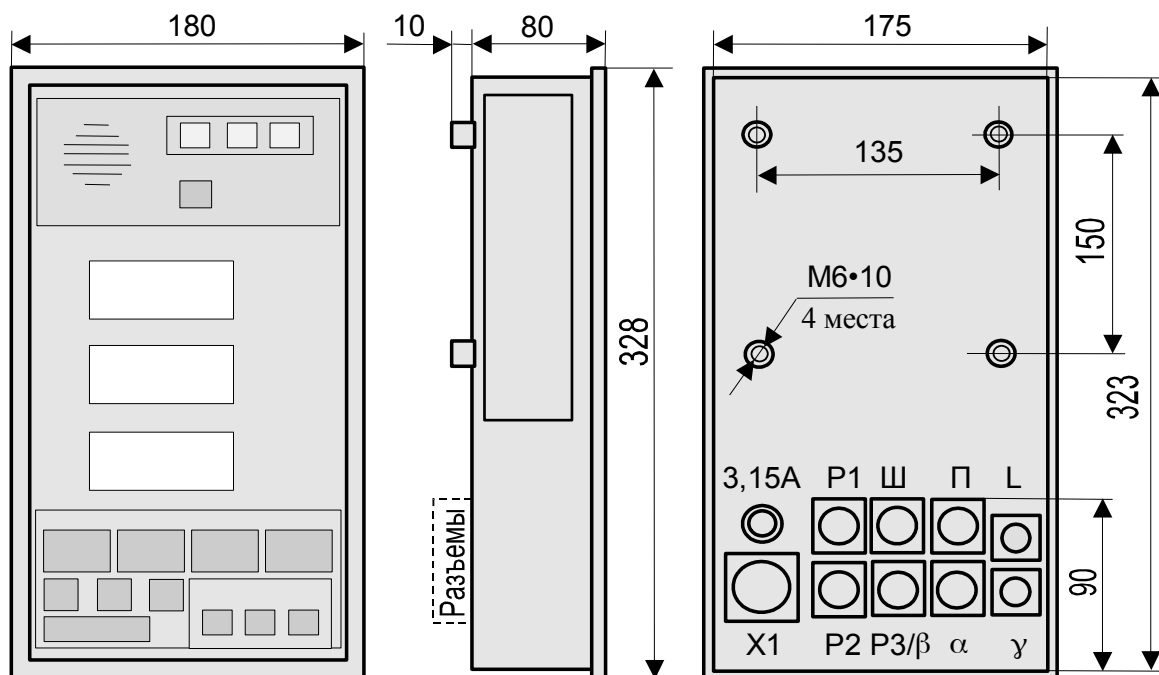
Габаритные и присоединительные размеры БОДа
